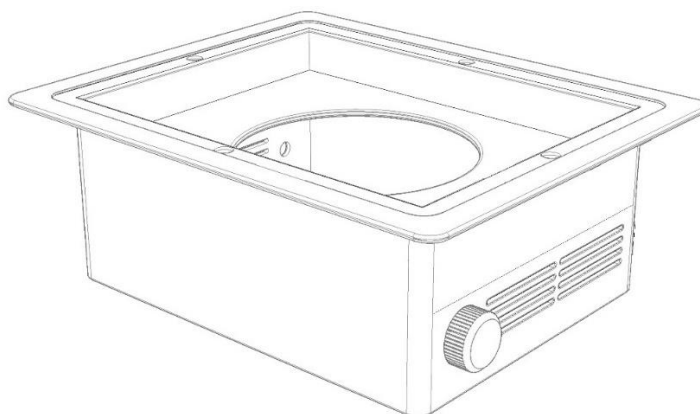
Ukázka 2 navrhovaného rastru, foto autor
